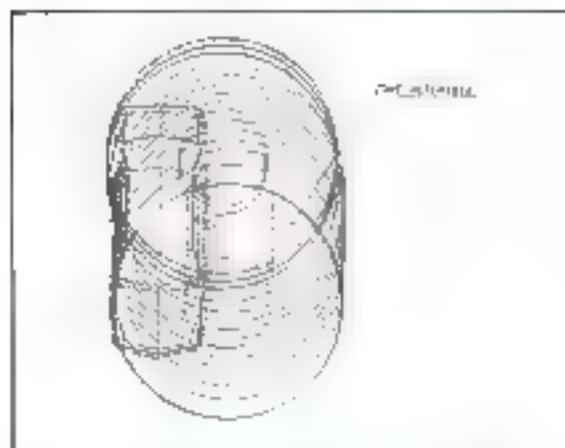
Positionnement du robot par rapport à la zone de soudure.
